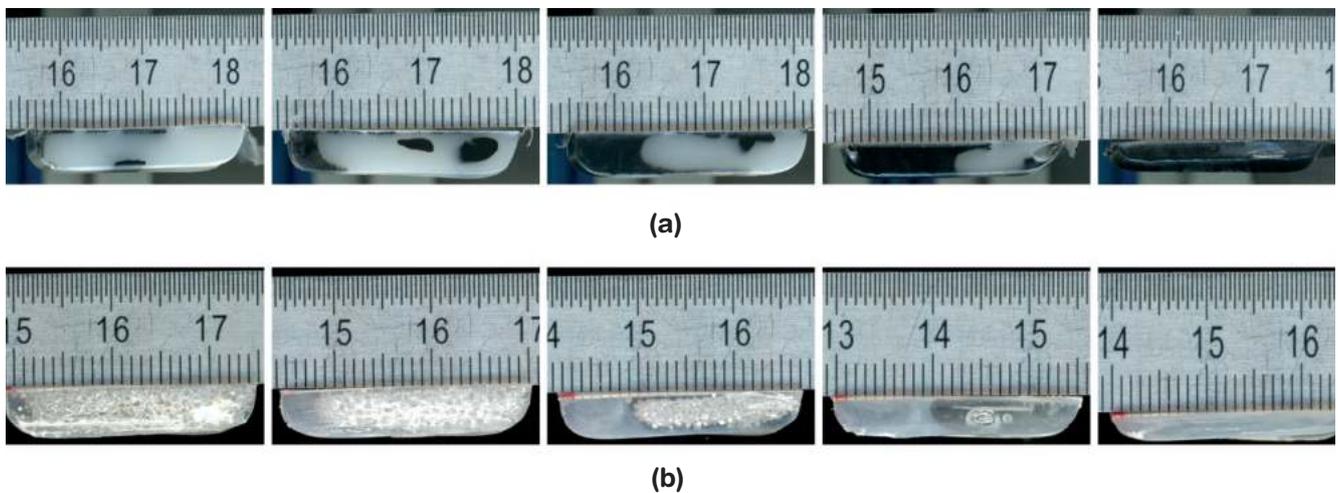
Schnittproben aus einer Dead-Stop-Untersuchung entlang der Aufschmelzzone in Extrusionsrichtung. (a) HDPE (b) PS [6]. Maßstab in Millimeter
